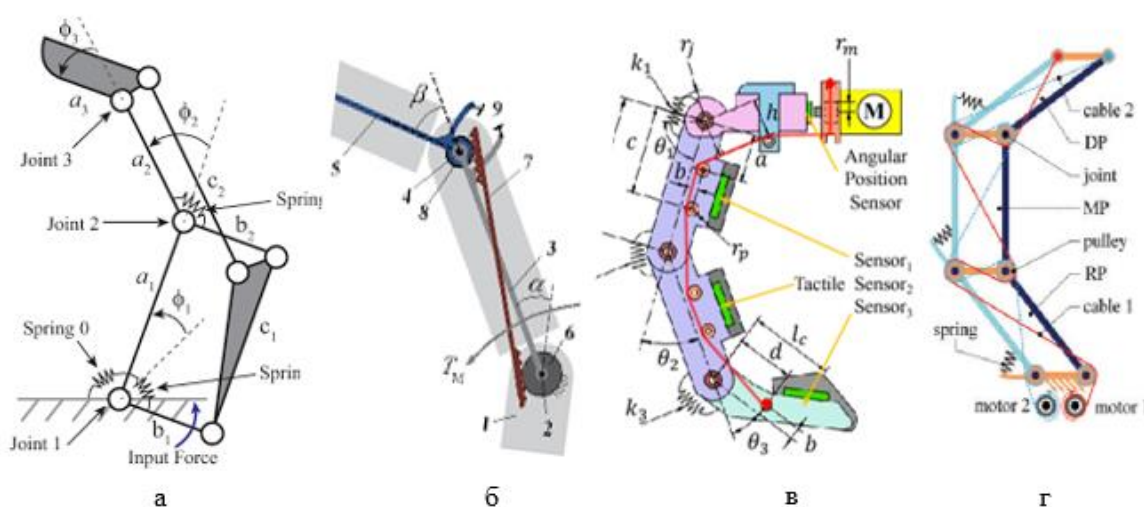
Исполнительные группы с групповым приводом и системой передачи движения выходным звеньям: а - рычажной [65]; б - зубчатой [57]; в - гибкой тягой [66]; б - комбинированной [67]
